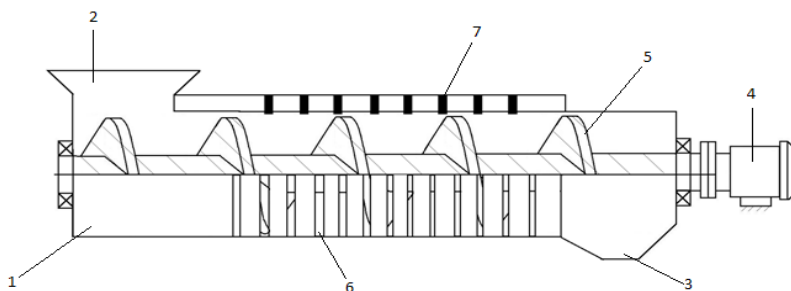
Предложенная схема установки непрерывного типа для очистки корнеплодов от загрязнений
